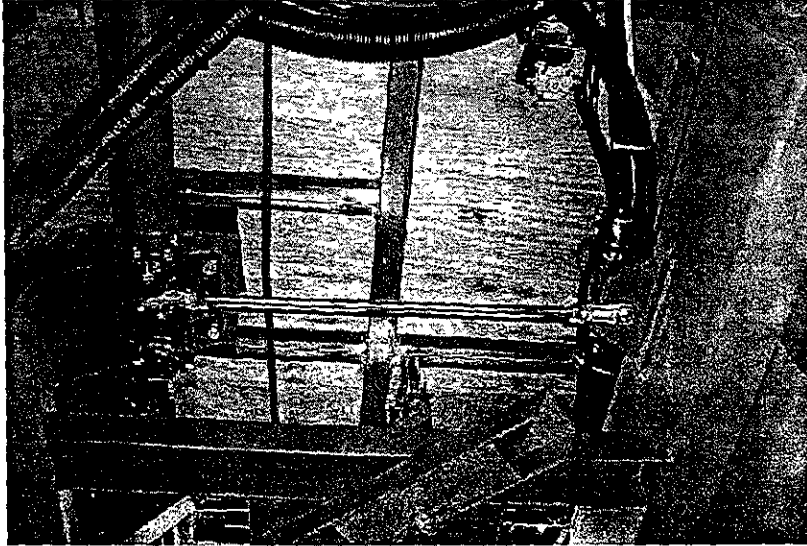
Ensamble final de tubo con ajustadores.
